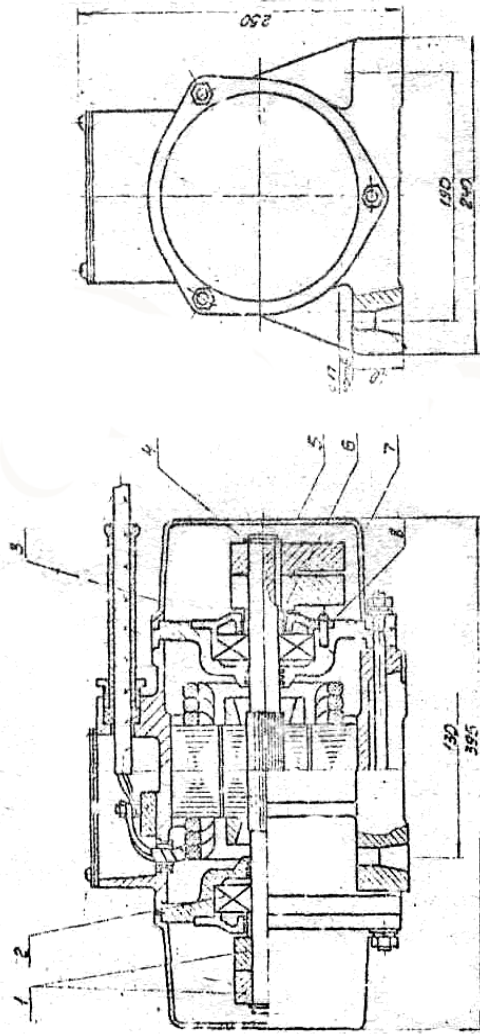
Вибратор общего назначения электромагнитный ИВ-128
